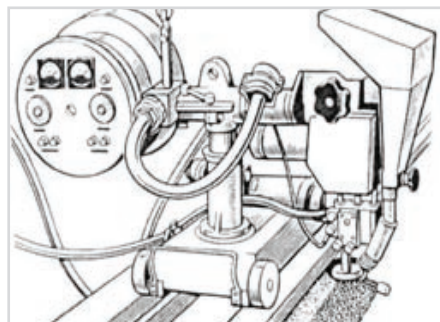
Сварочный трактор АДС-1000-2 выпуска 1952 г.
